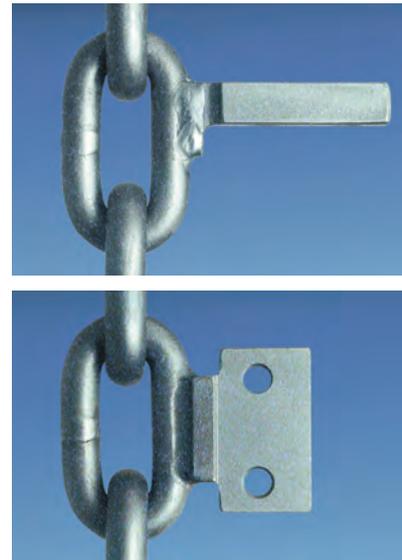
einzelne anschweißbare Mitnehmerfinger für innenverzahnte Kettenräder, geschmiedet, Kettenanlagestellen gehärtet
